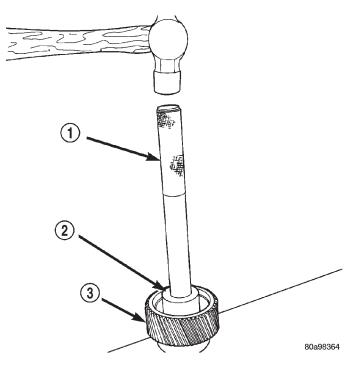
Instalación del cojinete de guía del engranaje impulsor
